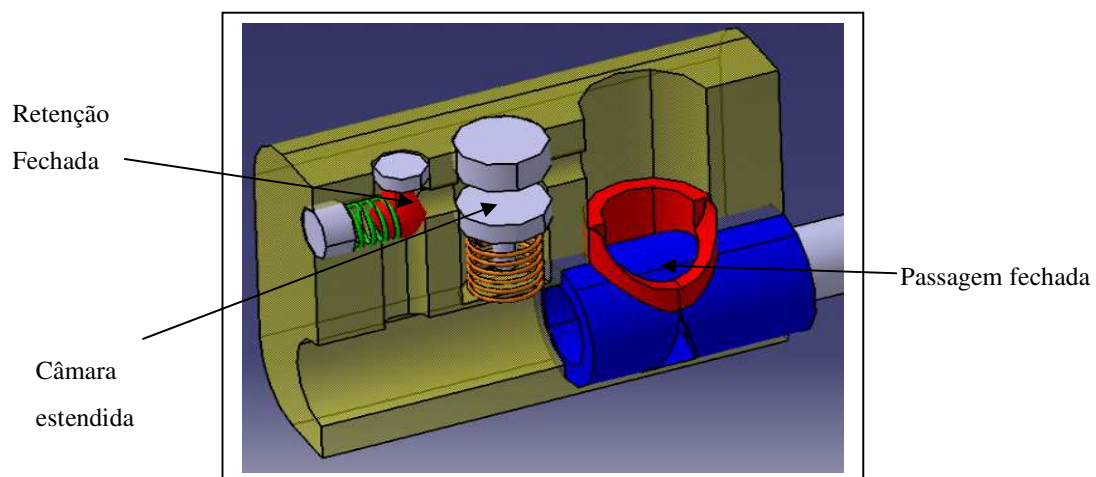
Válvula Fechada – Fase de Apoio.
